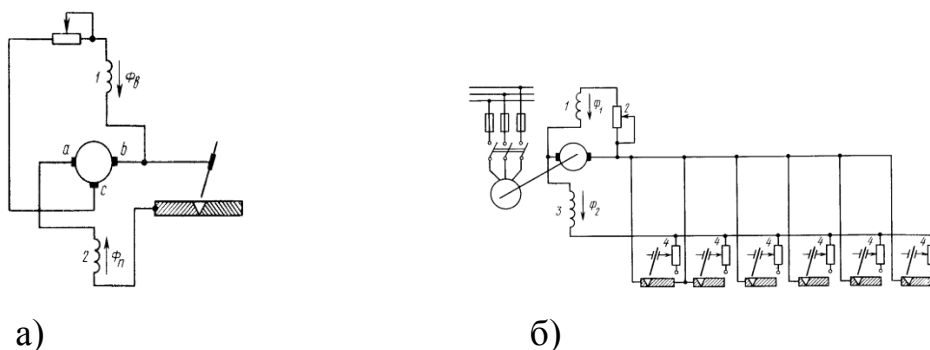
Схеми однопостового зварювального генератора з реактивною обмоткою а) і багатопостового з баластними резисторами б).
